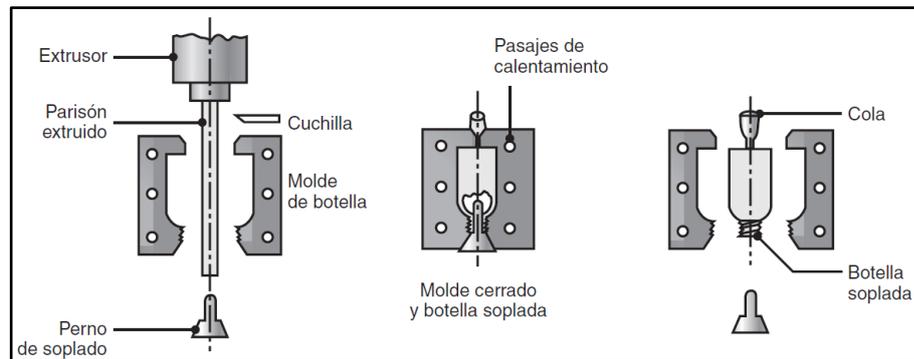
Proceso de moldeo por extrusión y soplado.
